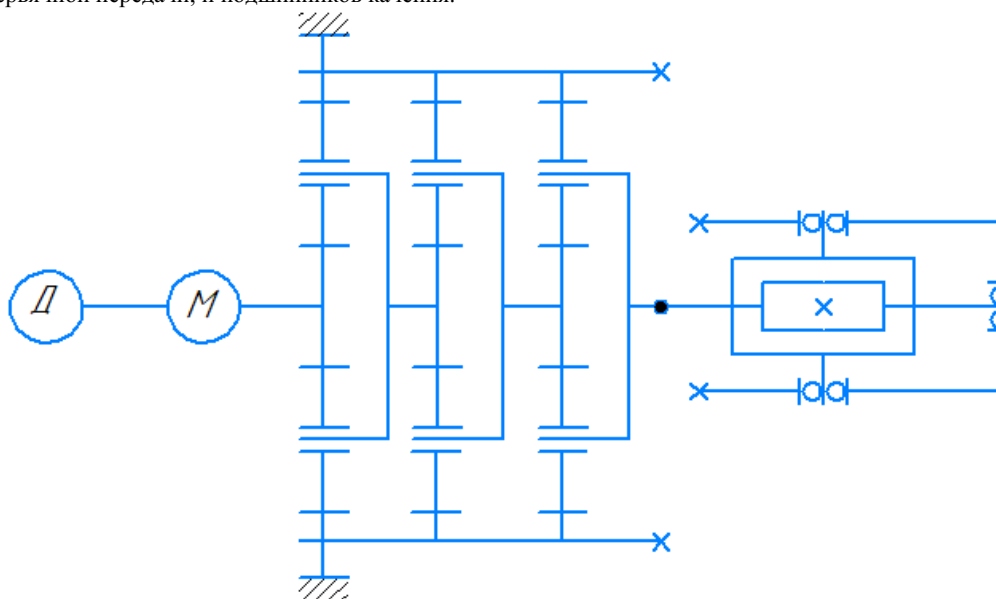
Кинематическая схема электропривода, слева направо: датчик, двигатель, планетарный редуктор, червячная передача со шкивами и подшипниками.
